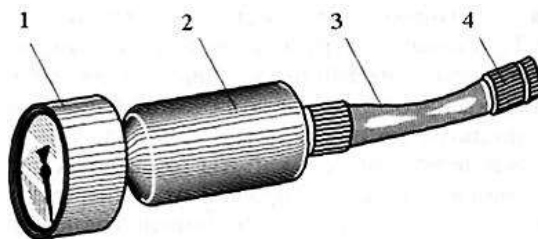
Пристрій КИ-28095: 1 – манометр; 2 – корпус; 3 – сполучний шланг; 4 – сполучний штуцер.
